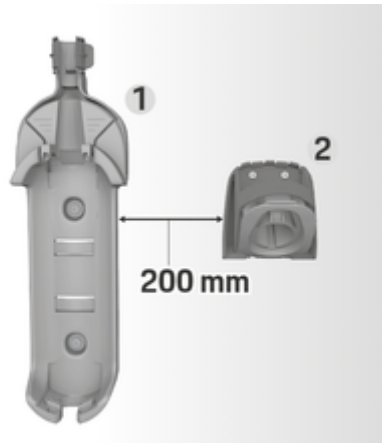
Abstand Wandhalterung – Steckerhalterung
